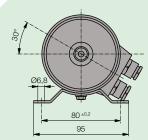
Befestigung mit Montagefuss. (Falls bei dieser Montageart die Stopfbuchse im Weg sein sollte, ist der KINAX WT 710 um 120° zu drehen, vorher sind die drei Rundmuttern am Getriebe zu lösen).
